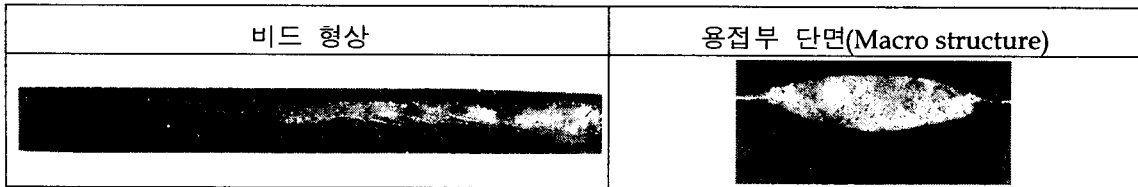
Bead on Plate 의 용접 형상 및 단면
